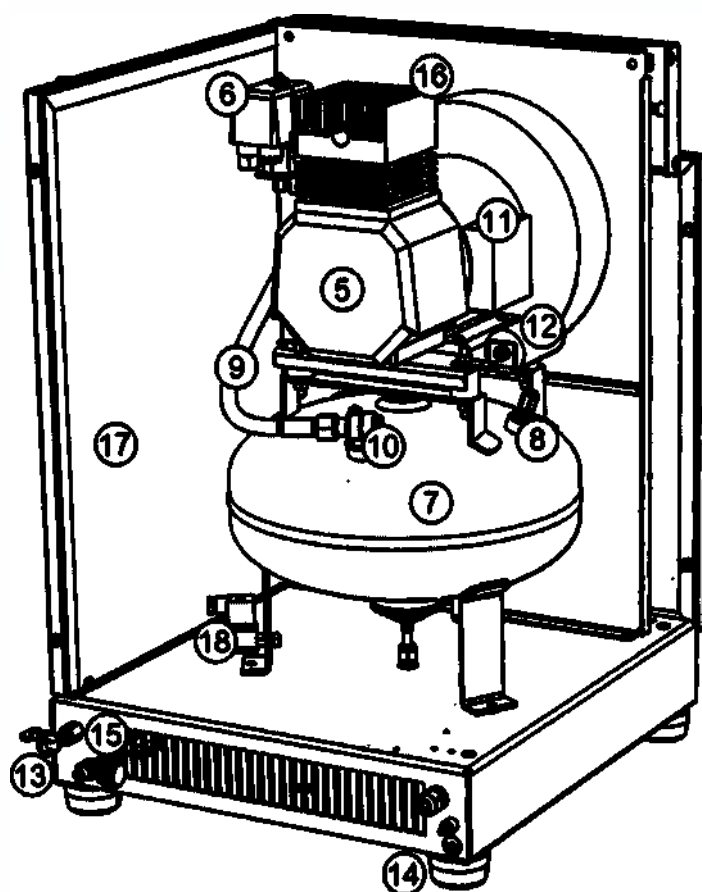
Общий вид компрессора KM-16.GMS150K
